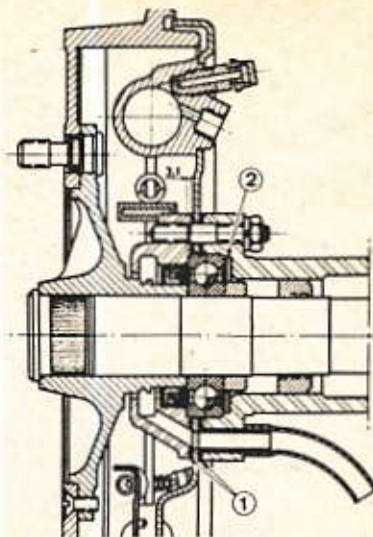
Montage d'un plateau de frein : 1. Joint de plateau - 2. Rondelle de réglage de 0,15 mm.
